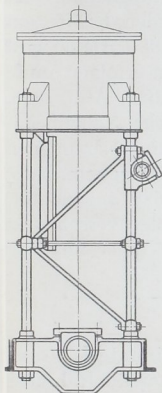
Rahmen für leichte Schiffsmaschinen.
